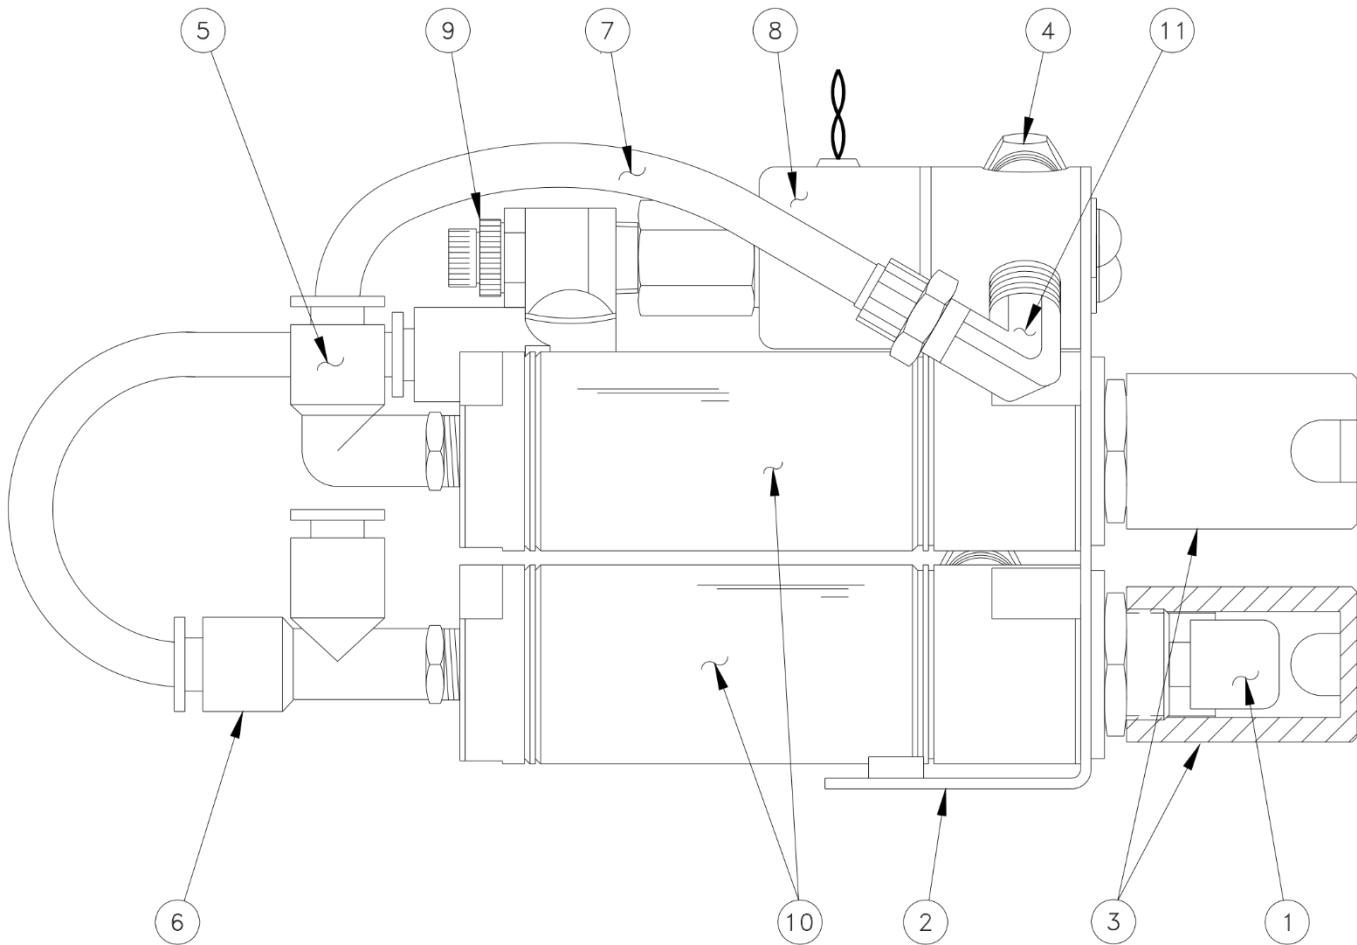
ENSEMBLE PIÈCE À MAIN N/P MB1083-3
